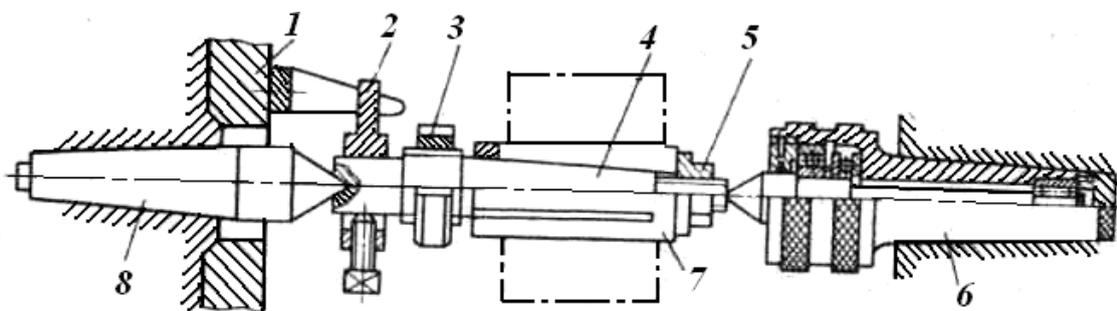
Резцовая оправка для обработки деталей над выемкой в станине
